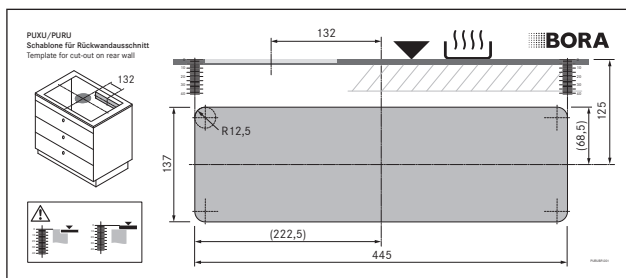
Dimenzije vgradnje pri obtočnem zraku, različica montaže A
